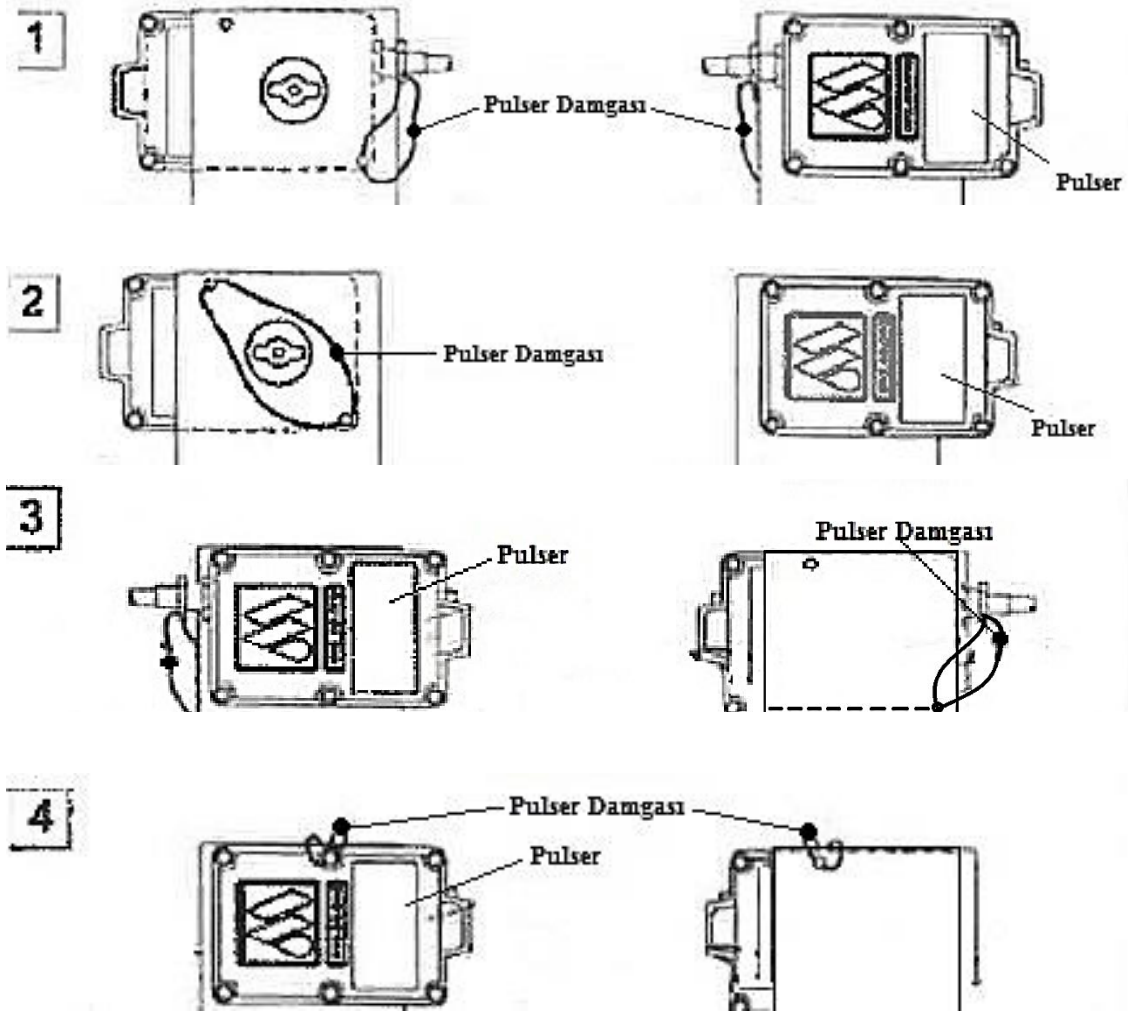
Brodimetre Pulser ve Montaj Damgası
